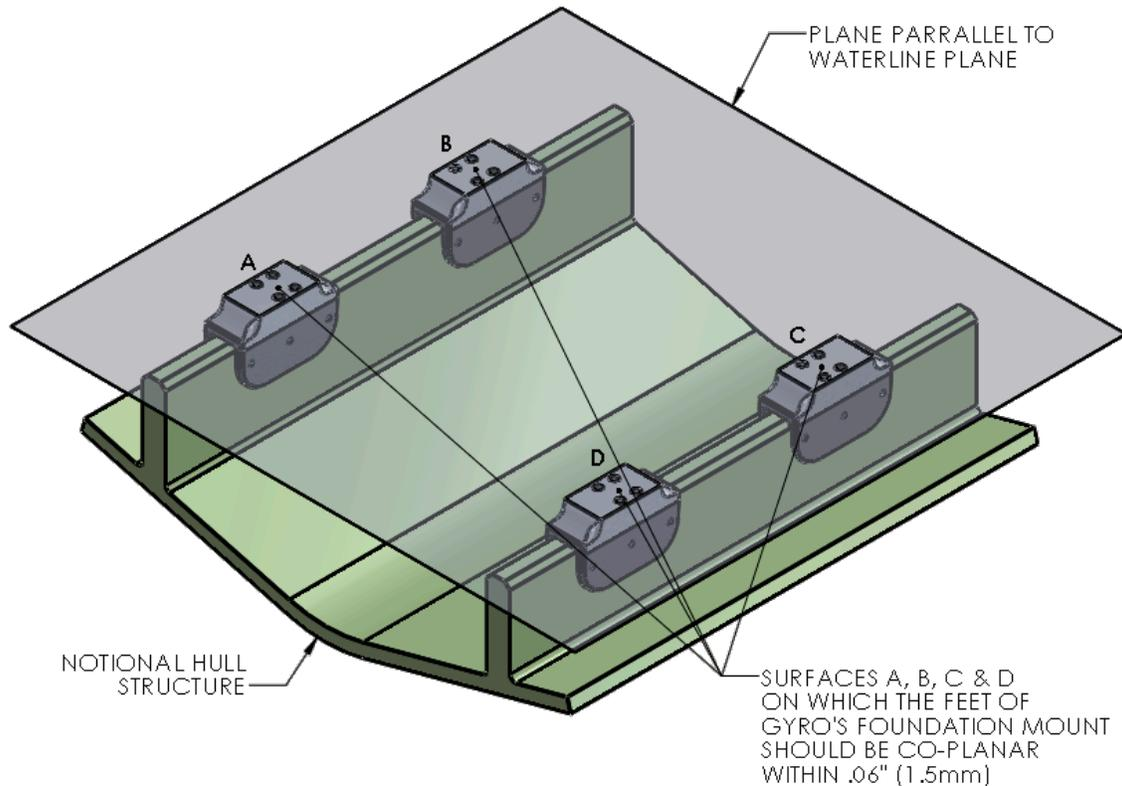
PROPRIÉTÉS COPLANAIRES DE LA FONDATION
